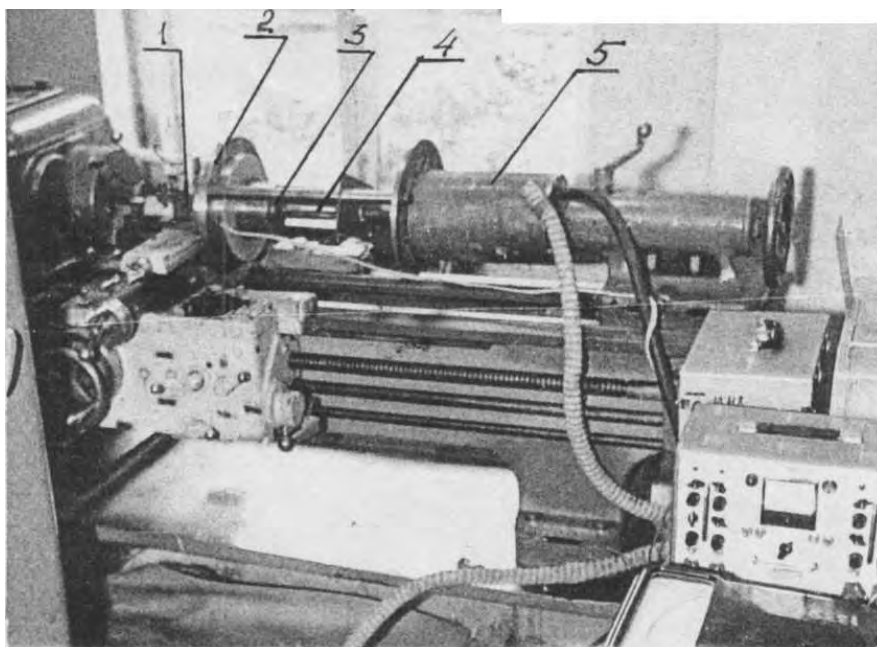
Установка для УЗД отверстий: 1 – установочное устройство; 2 – силоизмерительное устройство; 3 – деталь; 4 – инструмент; 5 – колебательная система
